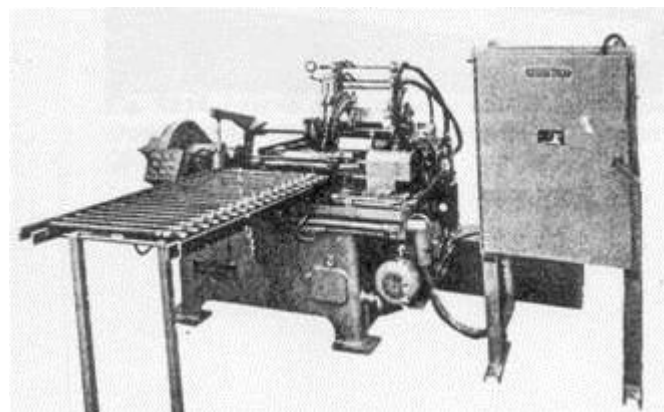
Máquina asentadora con mecanismo elevador hidráulico.
